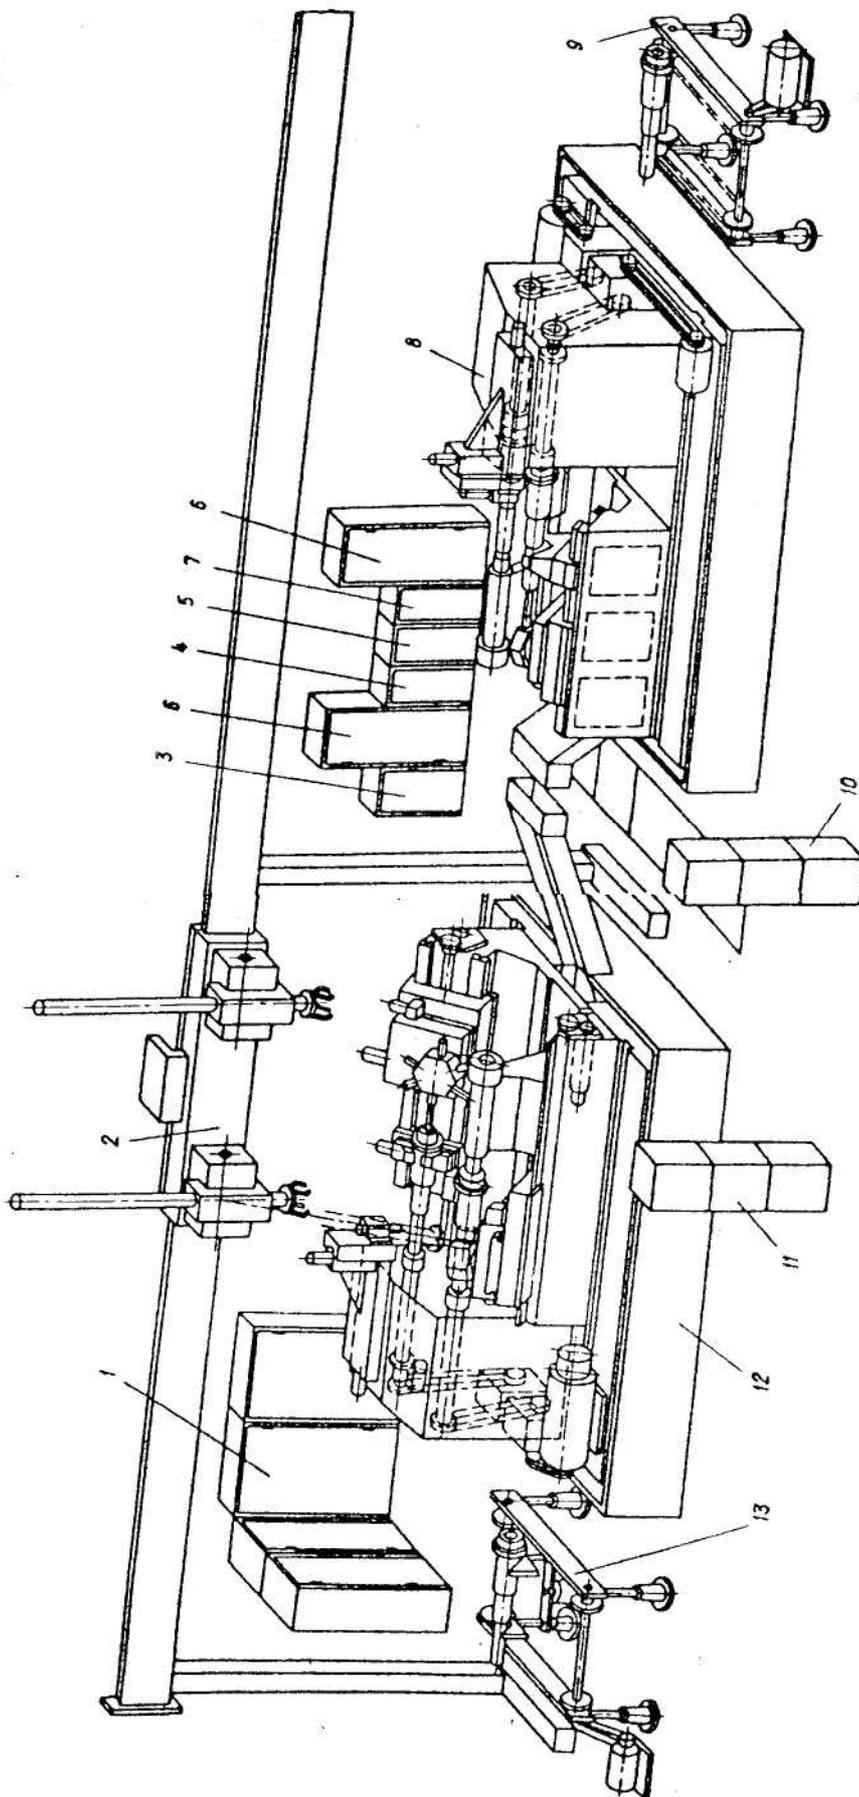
Роботизований комплекс із двома дзеркально встановленими двошвидковими модулями: 1, 6 – електрошафи; 2 – дворукий робот; 3 – система керування роботом; 4, 5, 7 – гідростанції для верстатів; 8, 12 – двошвидковий багатопільовий верстат; 10, 11 – системи ЧПУ; 9, 13 – станції завантаження заготовок і розвантаження деталей
